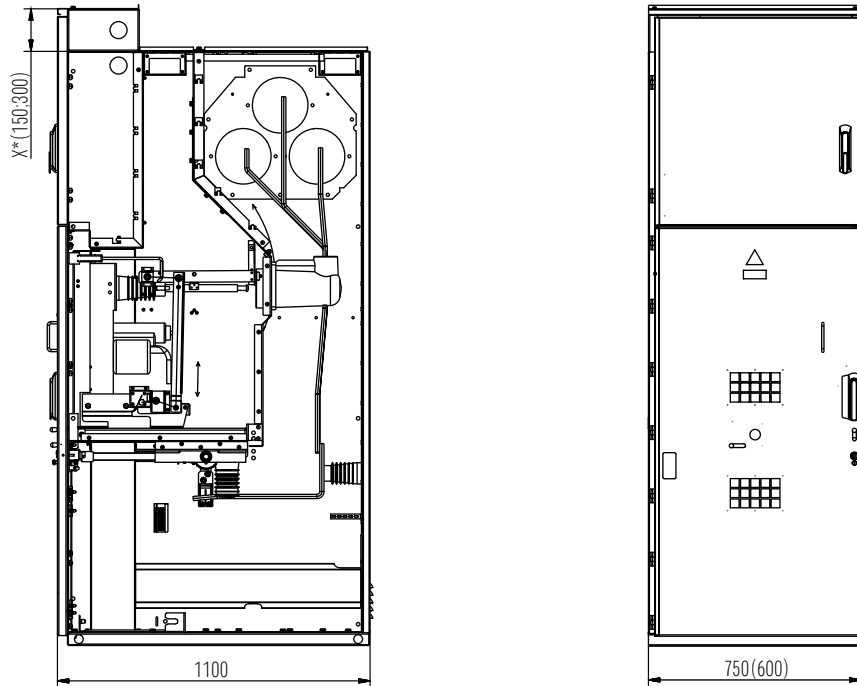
Шкаф КРУ D-12РТ с измерительными ТН и заземлителем сборных шин
